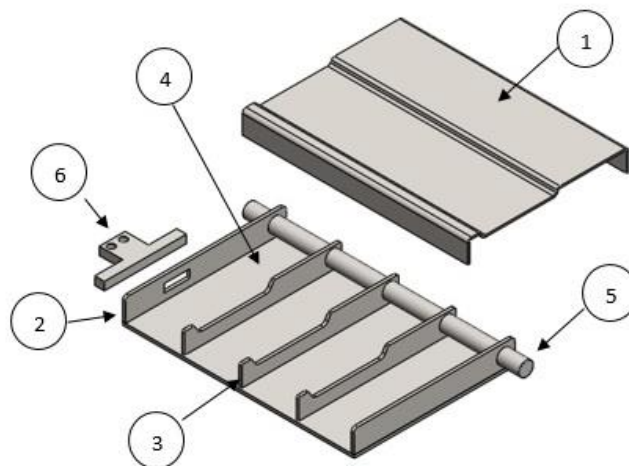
Vista explosionada Diseño Final Plataformas
